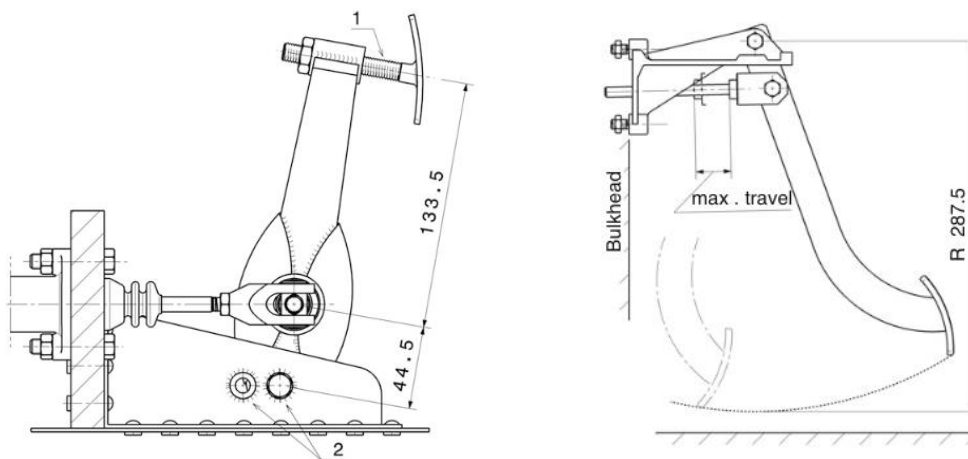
Posiciones de montaje del pedalier: Apoyado - Izquierda vs Colgante – Derecha
